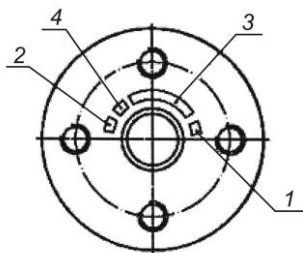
Расположение знаков маркировки и клейм на торце чистовой оси:
